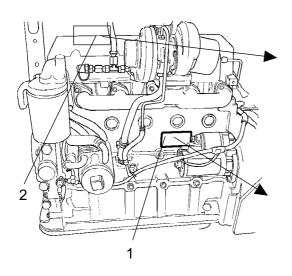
Typenschild 2. EPA-Schild (USA) Bei Ersatzteilbestellung bitte die Seriennummer des Motors angeben. Siehe auch Motorhandbuch.
